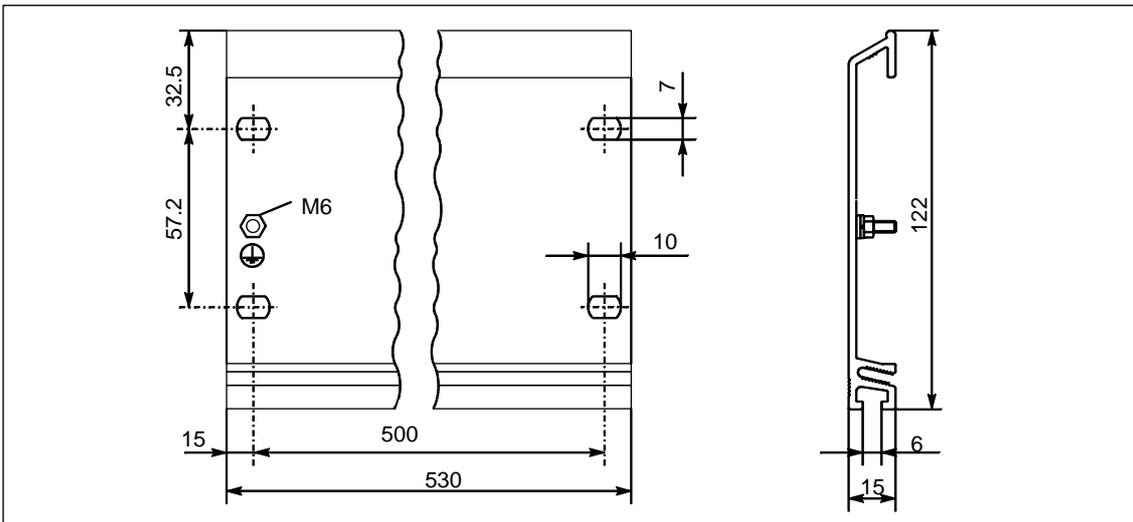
Чертеж с размерами профильной шины стандартной ширины 530 мм
